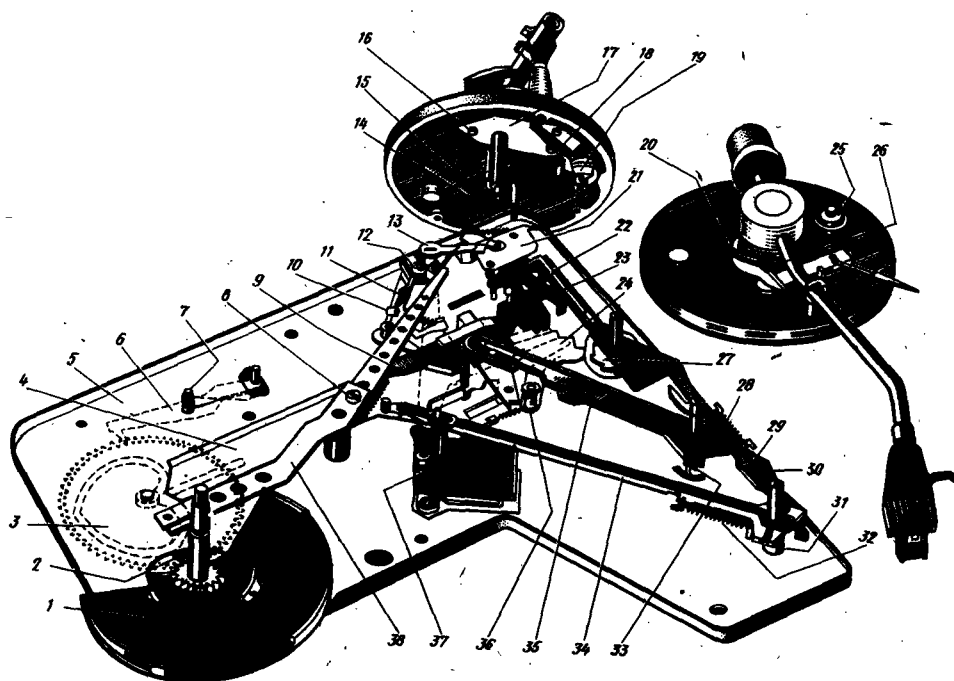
Кинематическая схема механизма автоматического управления звукоснимателя:
